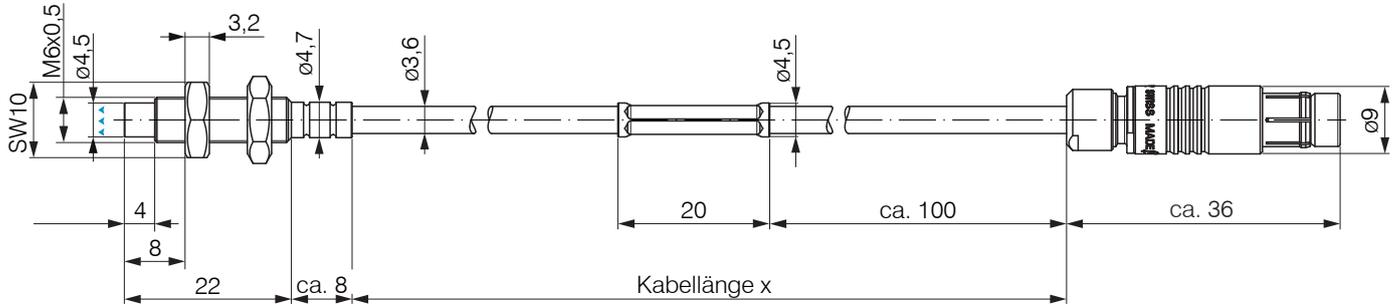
Maßzeichnung Sensoren ES-U1-C-CAX/mB0, Abmessung in mm
